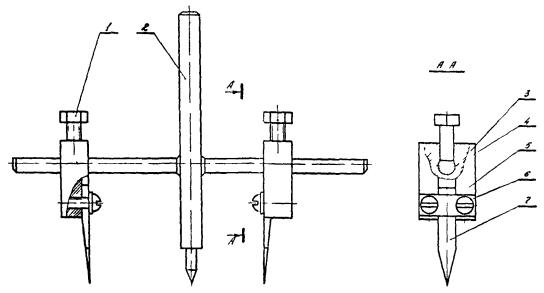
Приспособление для вырезки резиновых уплотнений:
